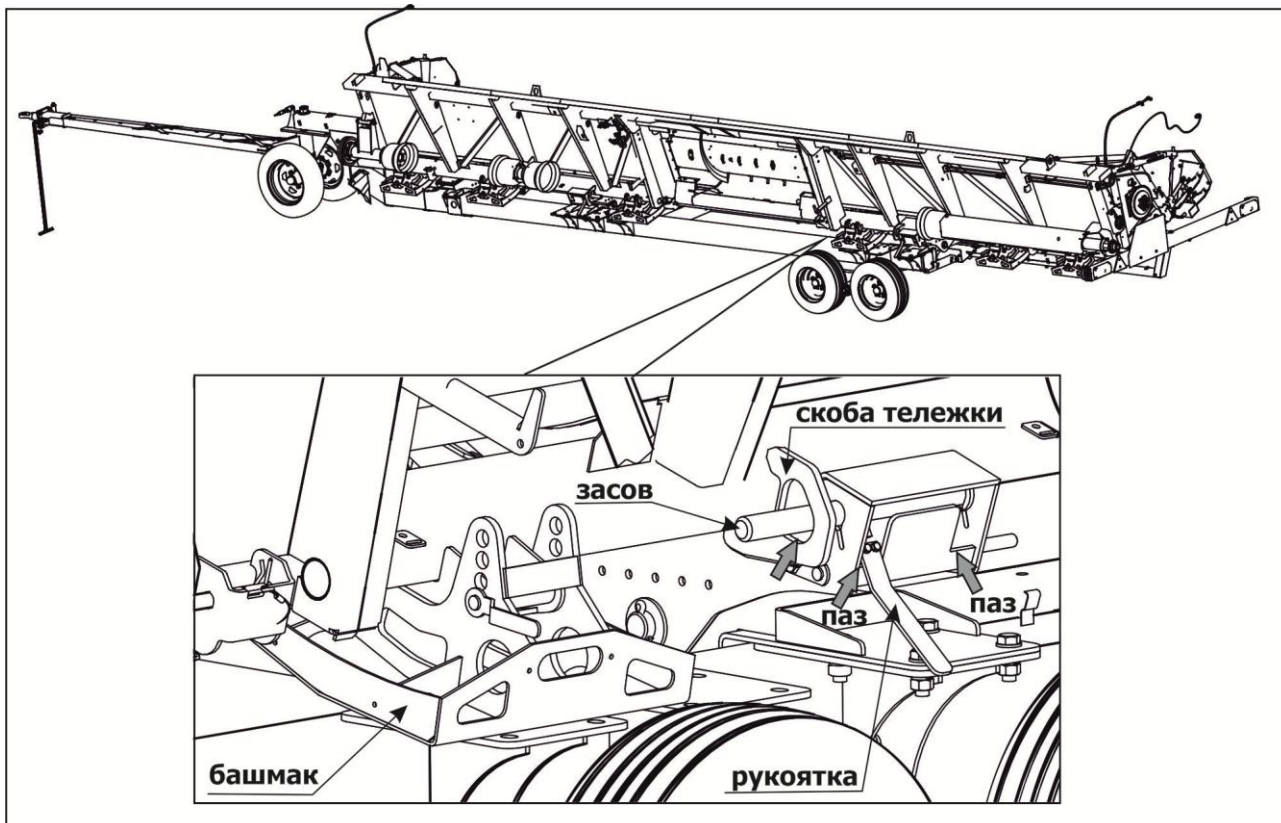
Установка жатки на на приспособление ППА-4000-05
